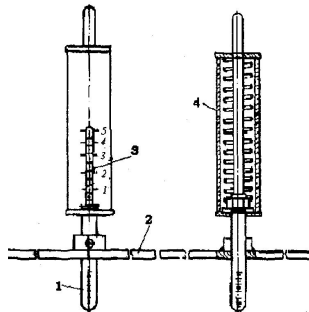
Динамометричний пристрій К-403 для перевірки натягу пасів: 1 – стержень; 2 – планка; 3 – шкала; 4 – корпус пружини
